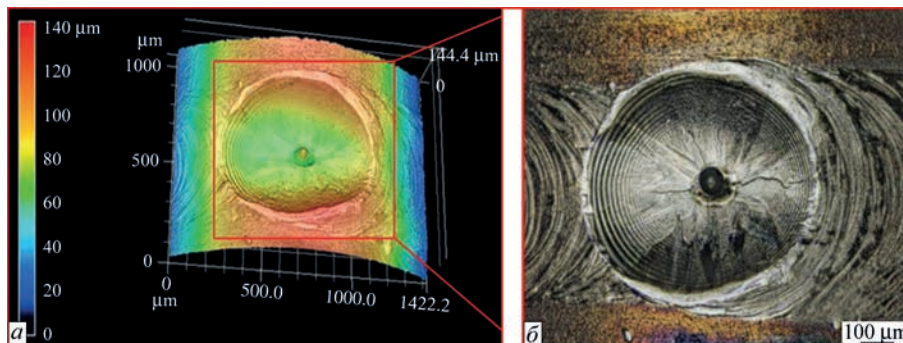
Кратер з тріщинами в кінці зварного з'єднання під час лазерного зварювання: 3D сканування кратера (а), вид зверху на кратер (б) [20]
